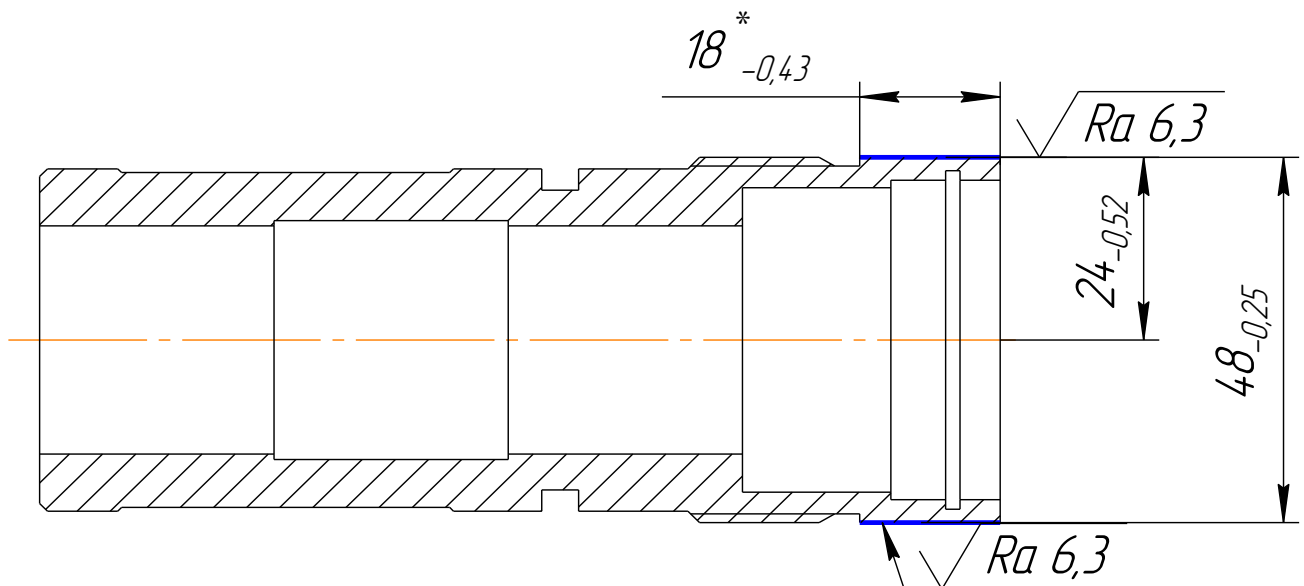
Ескіз фрезерної операції з ЧПУ
